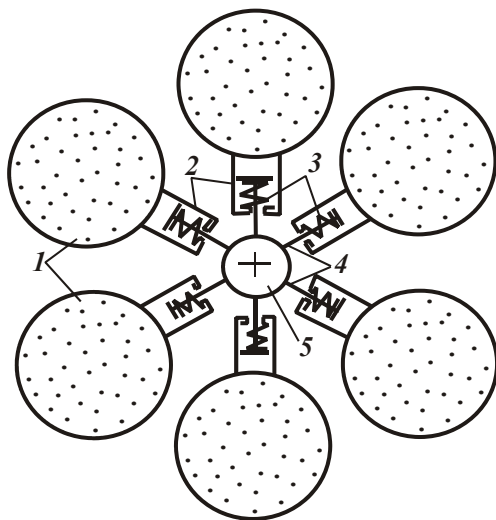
Инструмент для шлифования внутренних поверхностей: 1 – шлифовальный шар; 2 – цилиндр; 3 – пружина; 4 – штырь (спица); 5 – вал.
